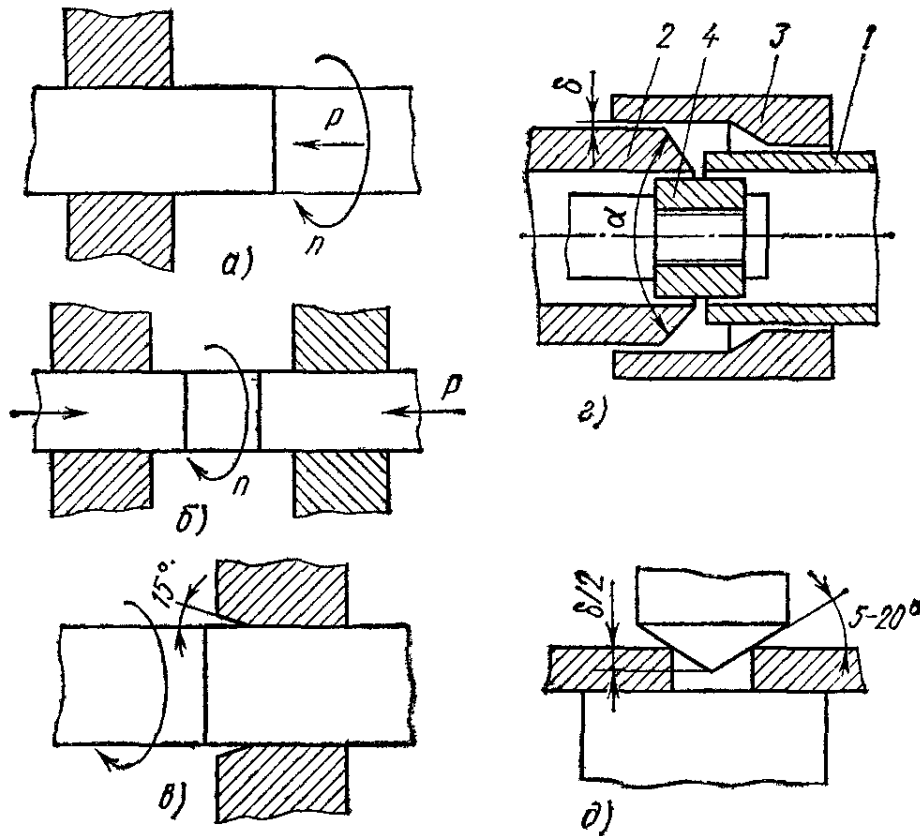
Схема сварки трением со свободным (а, б) и принудительным (в, г) формированием соединения, а также при Т-образной сварке (д)
